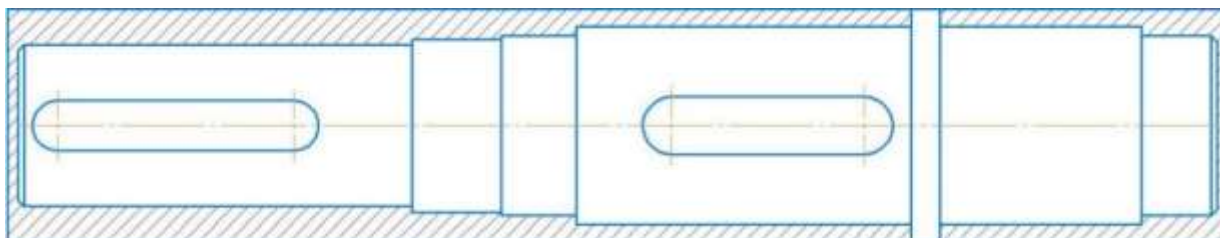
Ескіз заготовки «Вал тихохідний»
